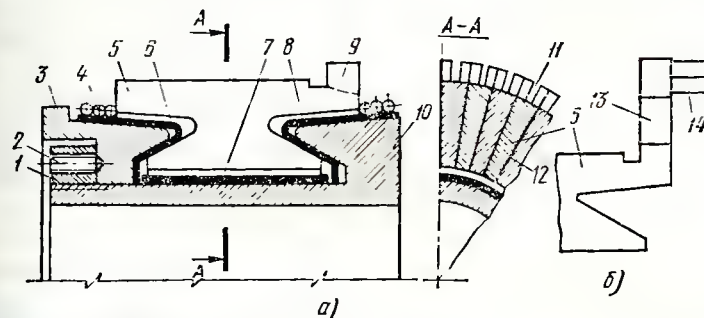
Коллектор с креплением нажимными кольцами и арочным распором (а) и пластина с ленточным петушком (б)
